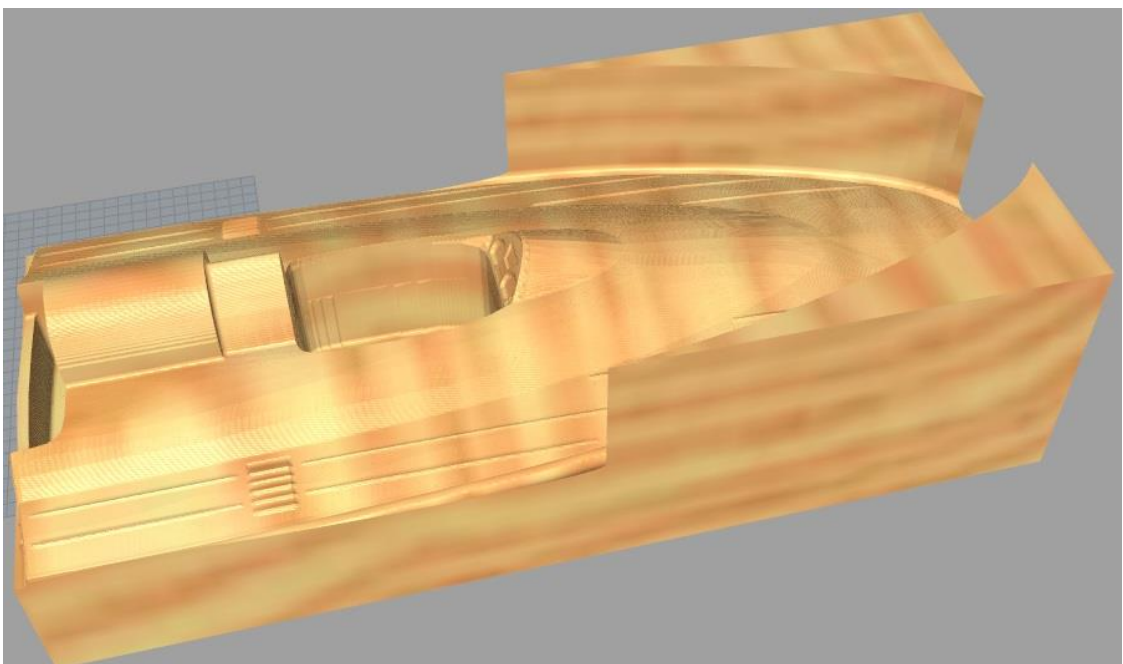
Анимированный вариант фрезеровки верхней части корпуса 3D-модели гоночной лодки
